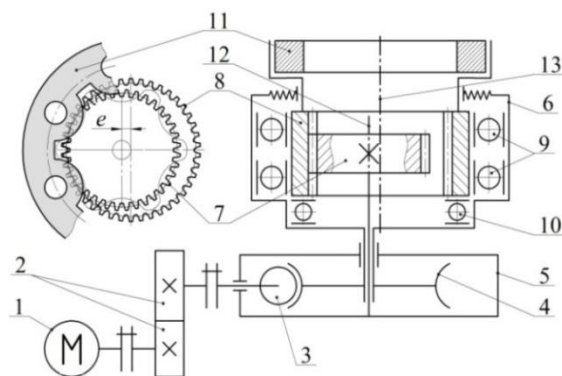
Кінематична схема пристосування для відтворення руху обкату: 1 – мотор-редуктор; 2 – зубчата передача ($z=11/z=35$); 3 – черв'як, 4 – черв'ячне колесо; 5 – корпус поворотного стола; 6 – еквівалентне колесо, що імітує сателіт; 8 – обойма із внутрішнім зачепленням; 9 – радіальні підшипники; 10 – упорний підшипник; 11 – оброблюване цівкове колесо; 12 – вісь обертання стола (вісь обкату); 13 – миттєва вісь обертання цівкового колеса
